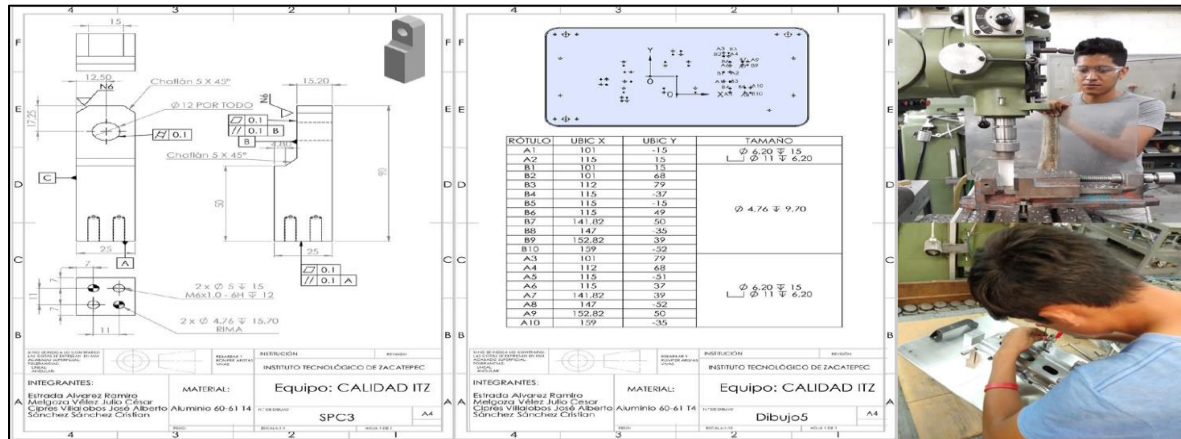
Diseño y desarrollo del proceso de fabricación del checking fixture
